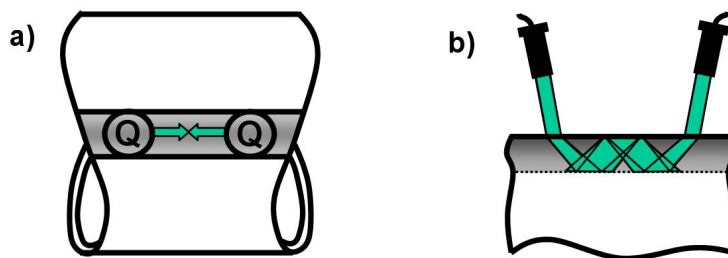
Prinzip der Querfehler-Prüfung, a) Prüfkopfpaar für die Querfehler-Prüfung direkt auf der Schweißnaht, und b) Seitenansicht mit Schnitt durch die Schweißnaht mit Winkeleinschallung zweier Prüfköpfe.
